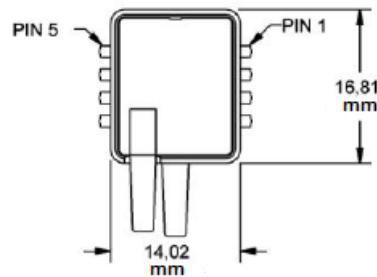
Pines y dimensiones del sensor de presión - fuente Hoja de datos sensor.
